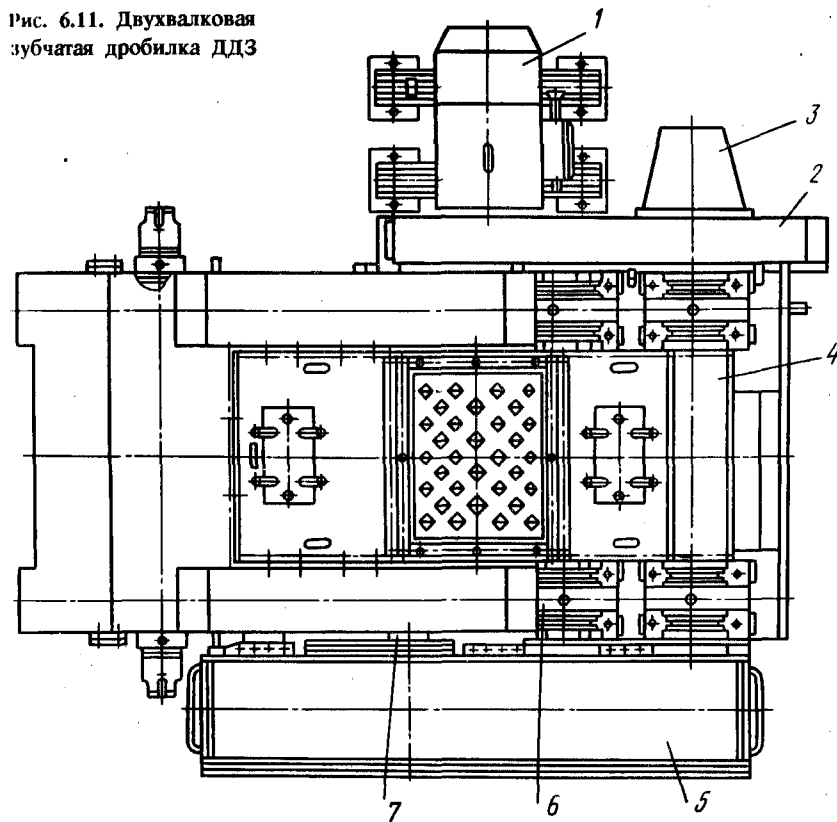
Двухвалковая зубчатая дробилка ДДЗ
